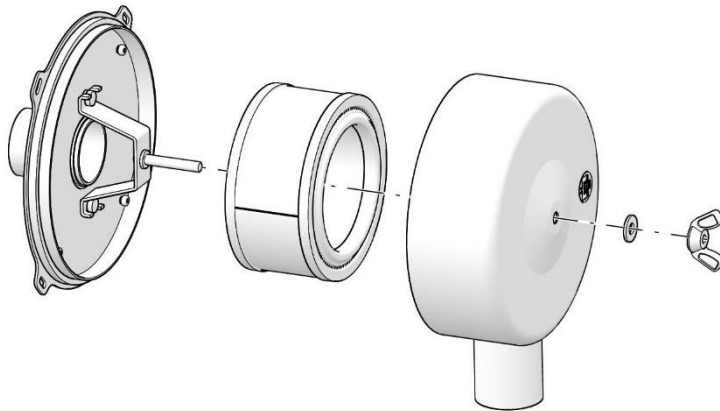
Reinigung des Gehäuses für das Sieb des Einlassfilters
